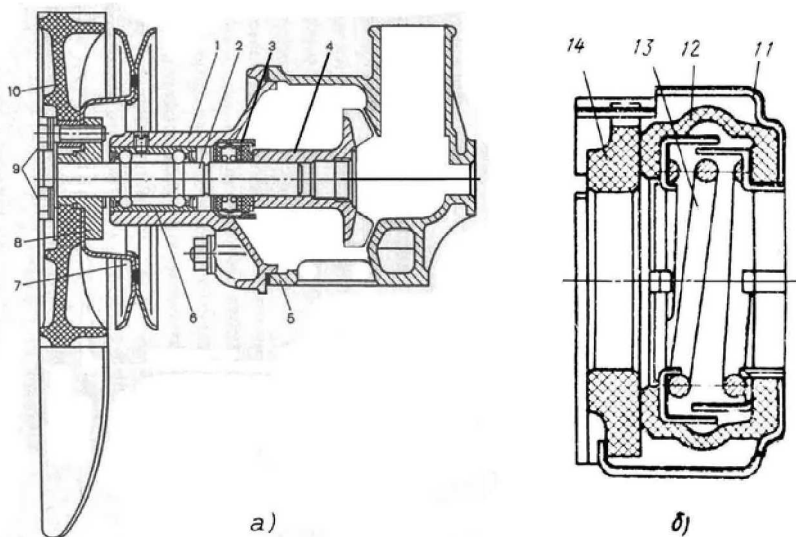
Конструкция насоса и вентилятора двигателей ВАЗ:
